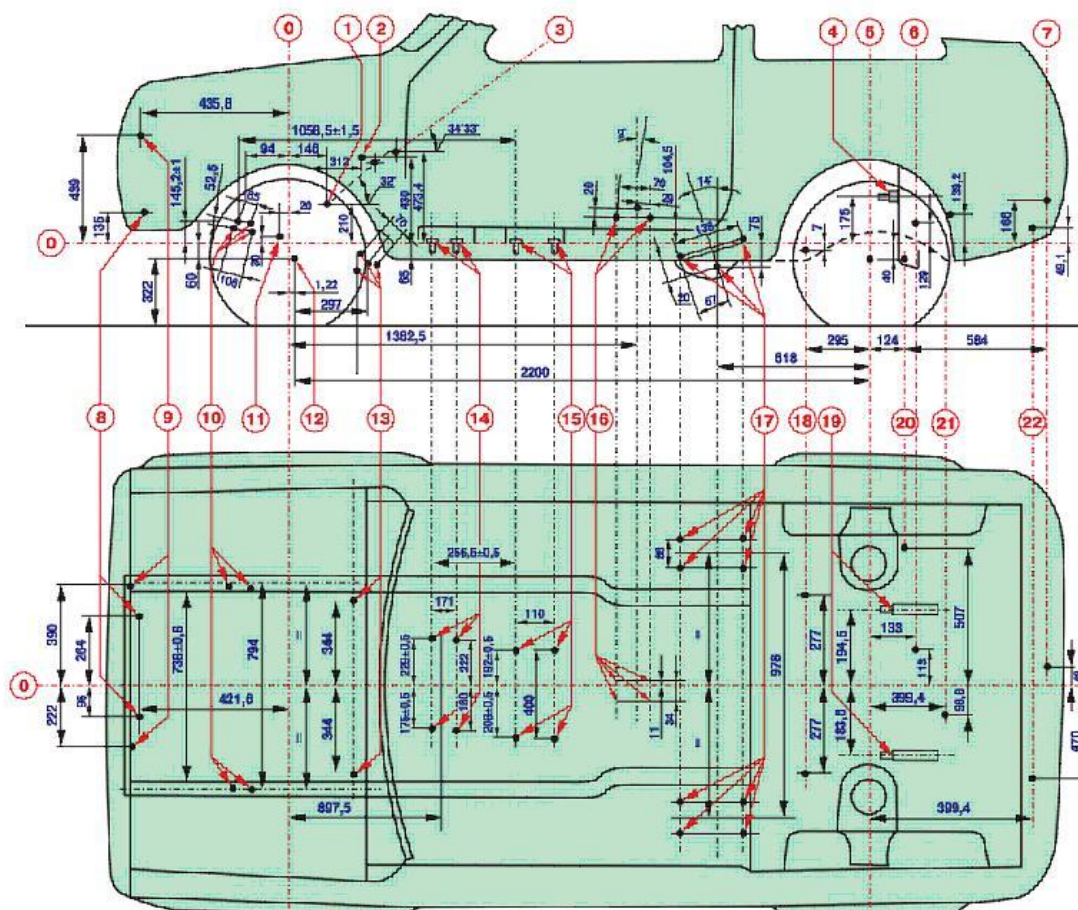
Контрольные точки кузова ВАЗ-2121
